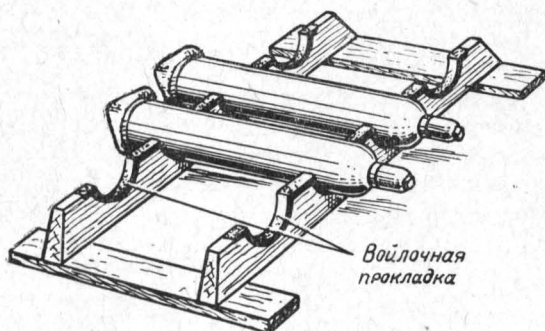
Приспособление для перевозки баллонов на автомобиле.
